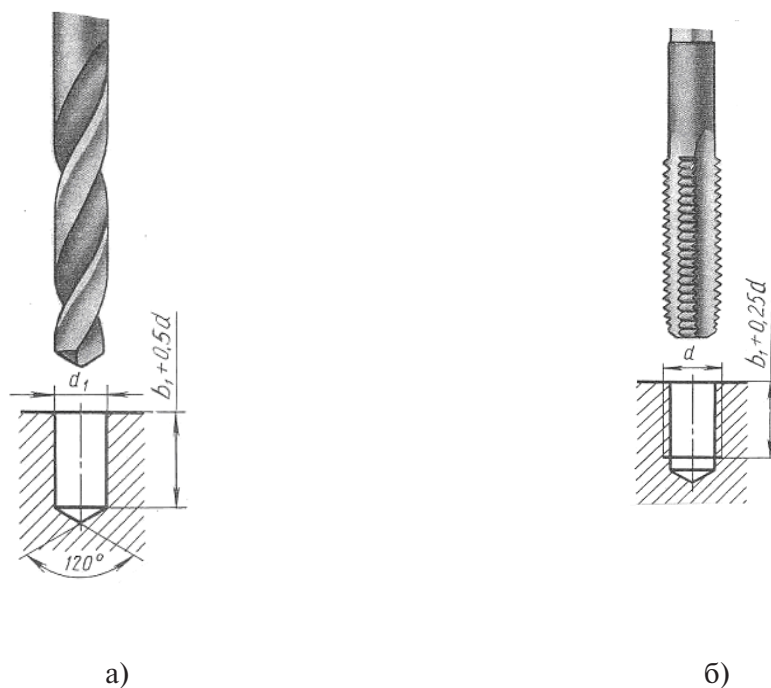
Последовательность изготовления внутренней резьбы: а – высверливание гладкого отверстия; б – нарезание резьбы метчиком
